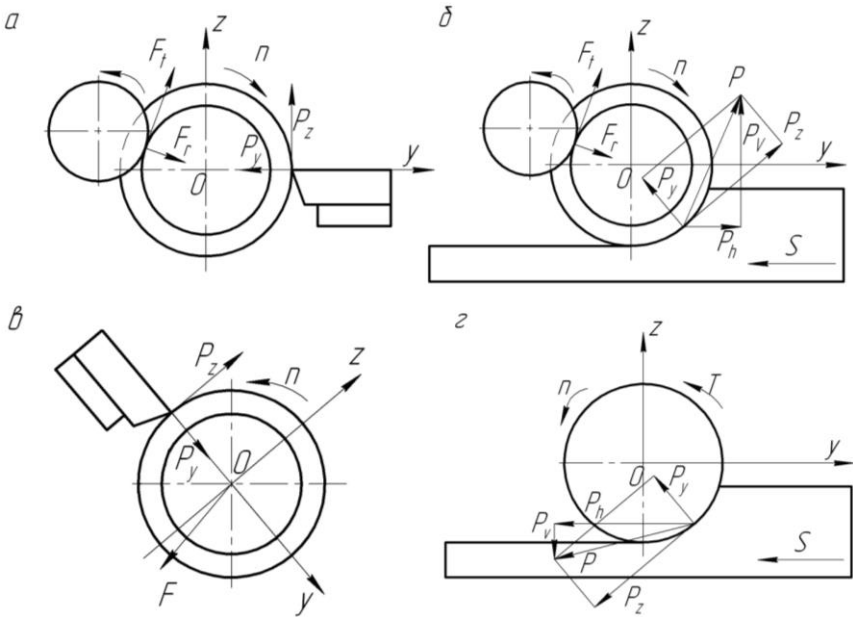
Расчетные схемы нагрузок на шпиндель от сил резания и приводного элемента в виде зубчатого колеса (а, б), шкива ременной передачи (в) и зубчатой муфты, шлицевого соединения или шкива на разгрузочном устройстве (з)
